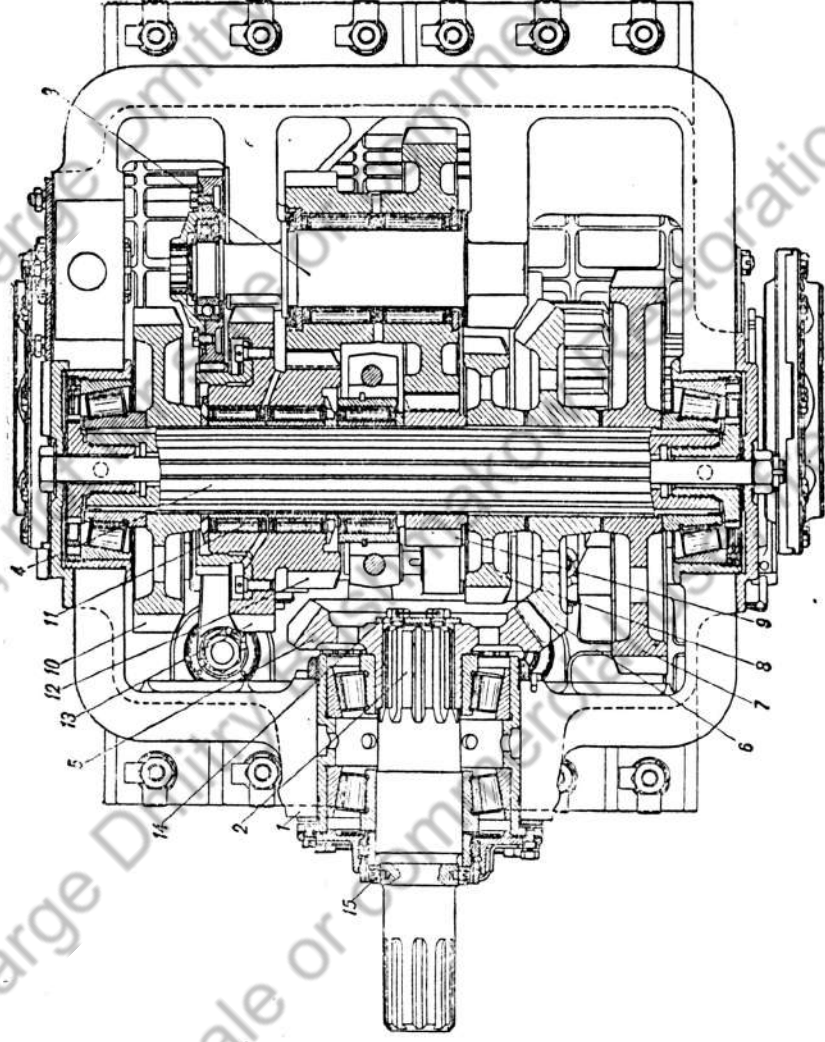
Разрез коробки по осям ведущего и промежуточного валов и оси блока шестерен заднего хода:
